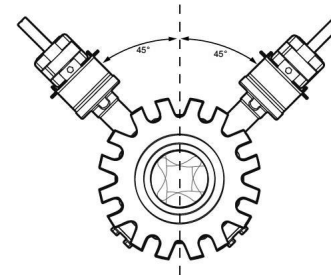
Zulässige Einbaulagen (beim Einbau in waagrechttem Rohrsegment)
